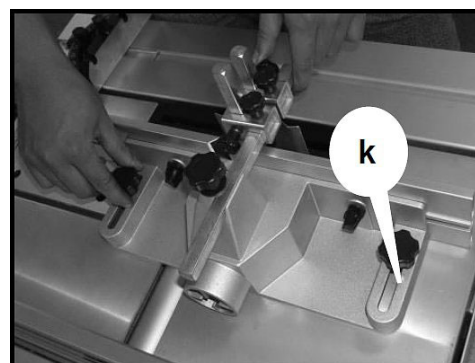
Fräs-Anschlag und Absaugvorrichtung befestigen
